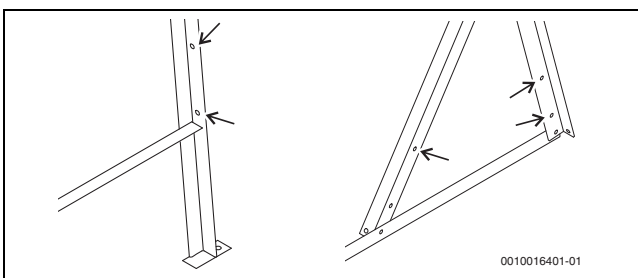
Ejemplos de montaje del cable de puesta en tierra en el soporte de montaje (izquierda MTSS, derecha: WSF)
